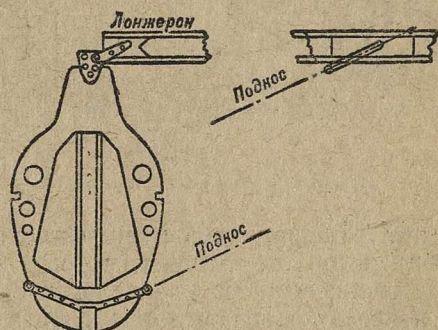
Центральный шпангоут круглого фюзеляжа и схема крепления к нему крыла у подкосного планера Г-9
